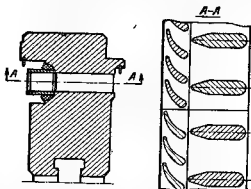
Сварная диафрагма 3-й ступени турбины ВКТ-100 новой конструкции с силовыми ребрами и облегченным швом сварки лопаточного аппарата с телом и ободом диафрагмы.
